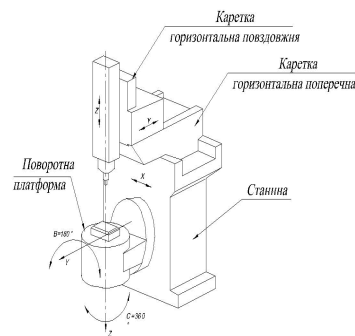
Вертикально-фрезерний консольний верстат із поворотною платформою (столом)
